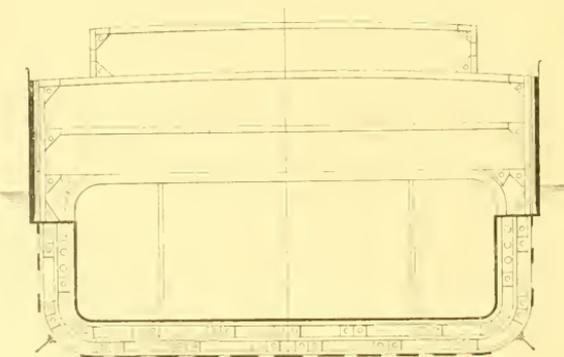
Coupe transversale d'un vaisseau de ligne avec triple fond et cuirasse protectrice sous-marine.
